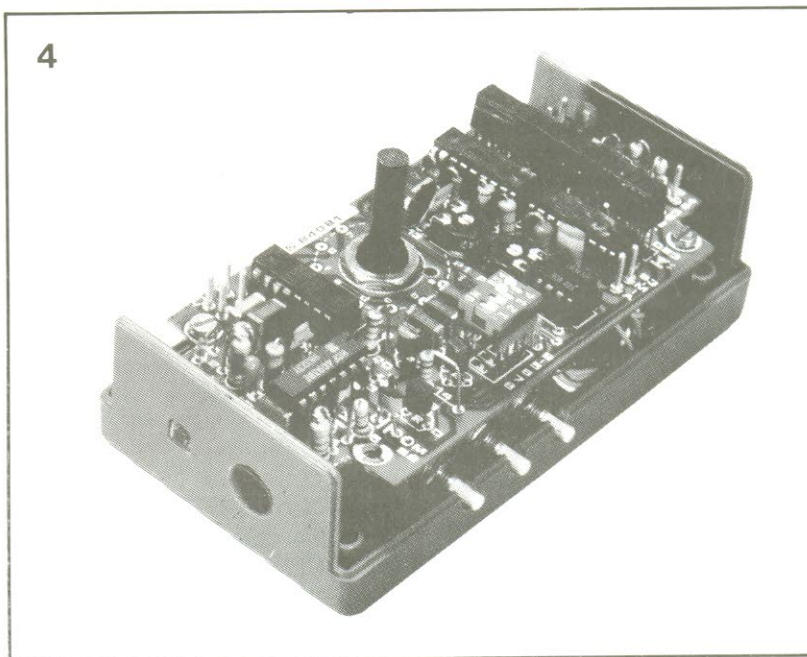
A placa do circuito impresso deve ser montada sobre separadores para deixar espaço para a bateria, os botões de pressão e o corpo de S2.
